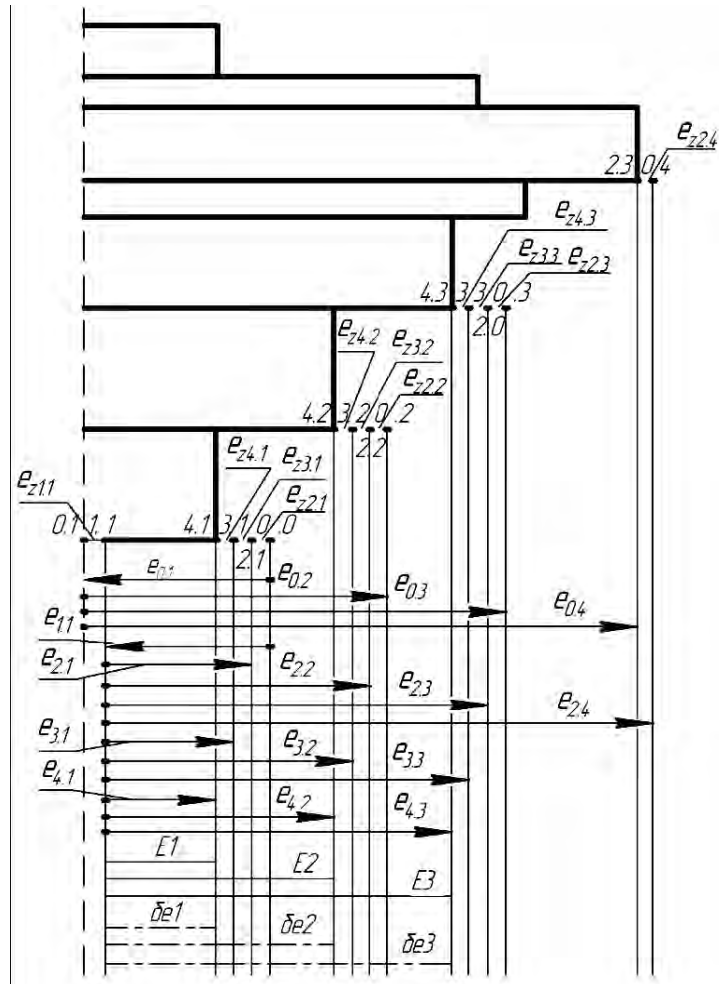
Расчетная схема обработки вала для определения эксцентриситетов припуска
